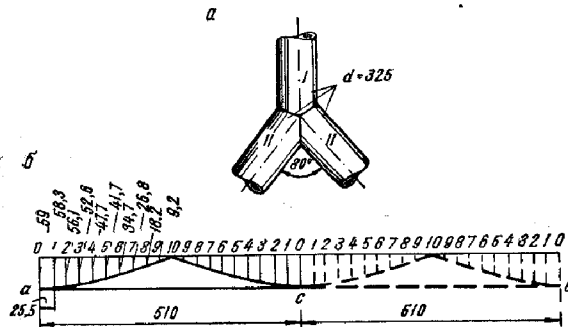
Сварной тройник разветвленный (штаны).
